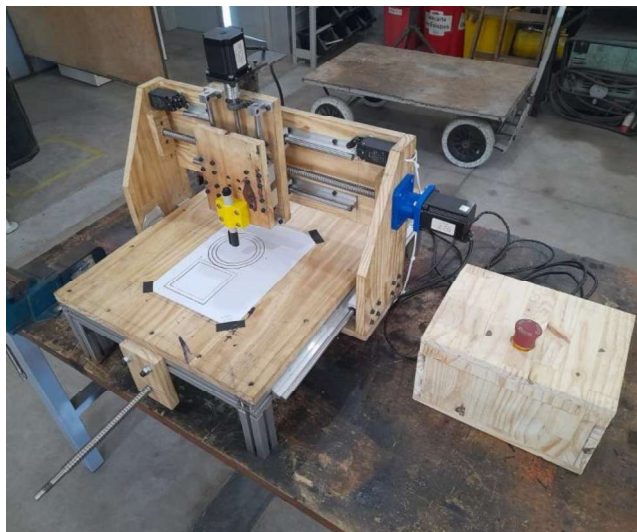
montagem completa da máquina CNC (partes mecânicas e elétricas)
